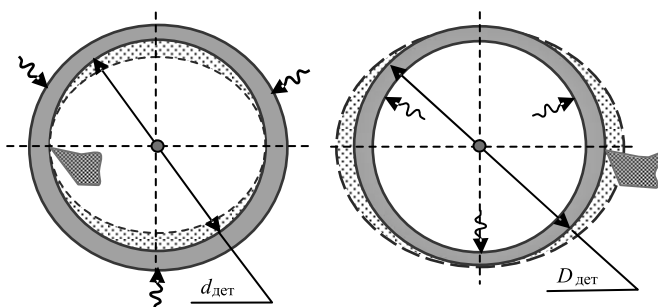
Схемы предварительной механической обработки трубчатой заготовки:
